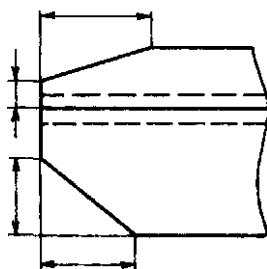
Простановка размеров скосов деталей металлоконструкций
